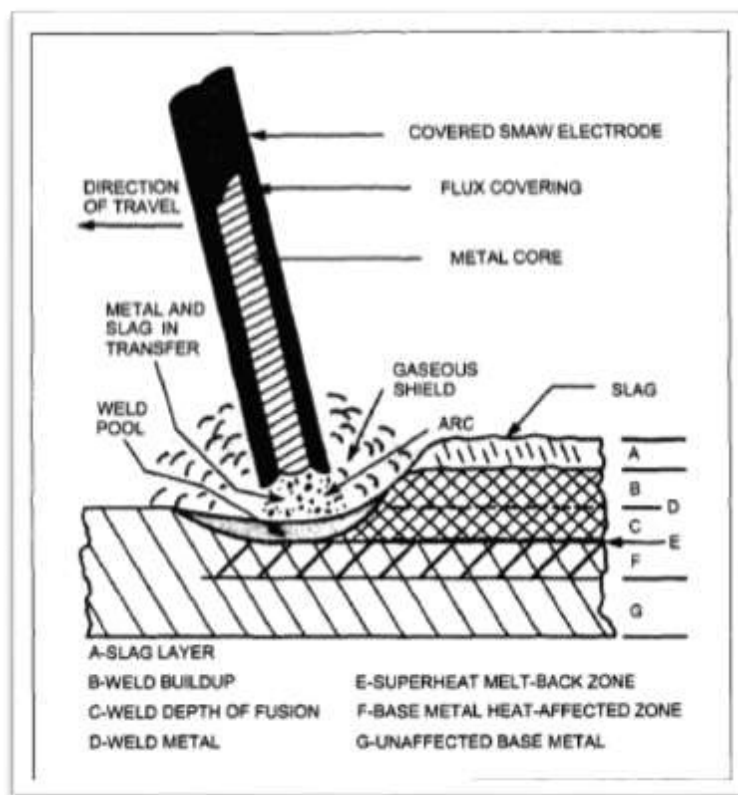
Representación esquemática de la soldadura SMAW (Fuente: Welding Handbook)
